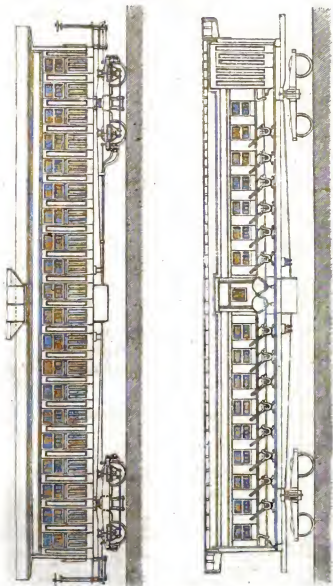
Élévation et coupe longitudinale d'un wagon américain.
